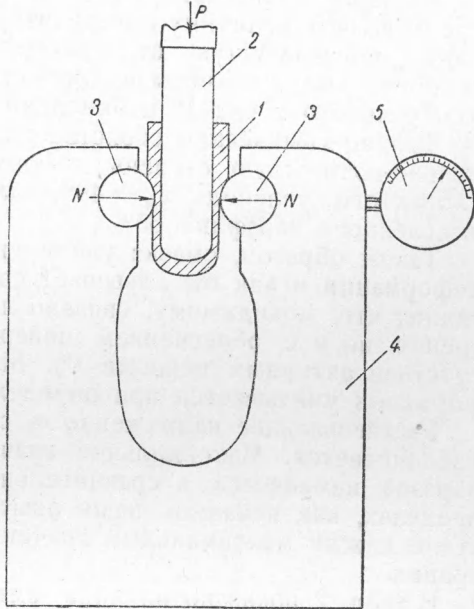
Схема метода. 1 — образец (полоска металла), 2 — плоский пуансон, 3 — круглые цилиндрические матрицы, 4 — жесткий динамометр (упругая скоба), 5 — индикатор
